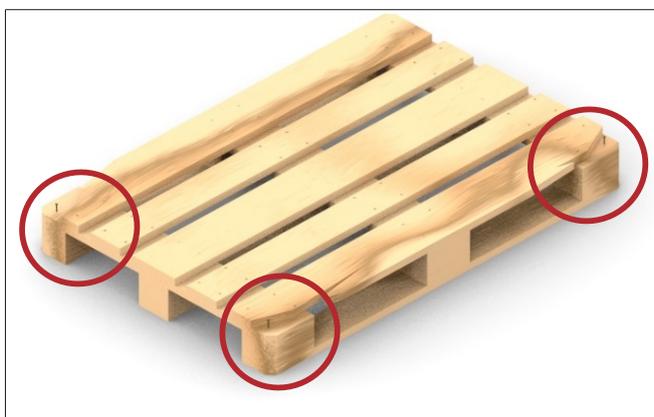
si plus de deux planches de fond ou supérieures ont des éclats tels qu'on peut entrevoir plus d'un fût de clou.
